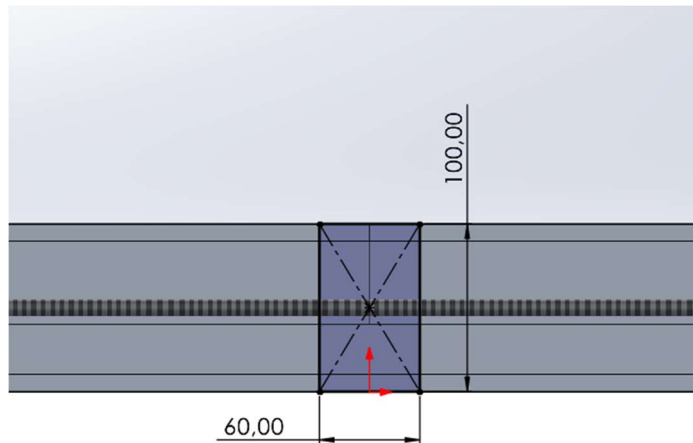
Dimensiones generales de los perfiles de la zona inferior del conjunto.
